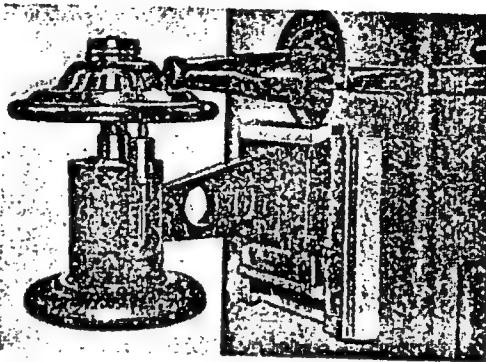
Приспособление для ультразвуковой сварки малых металлокерамических контактов.
